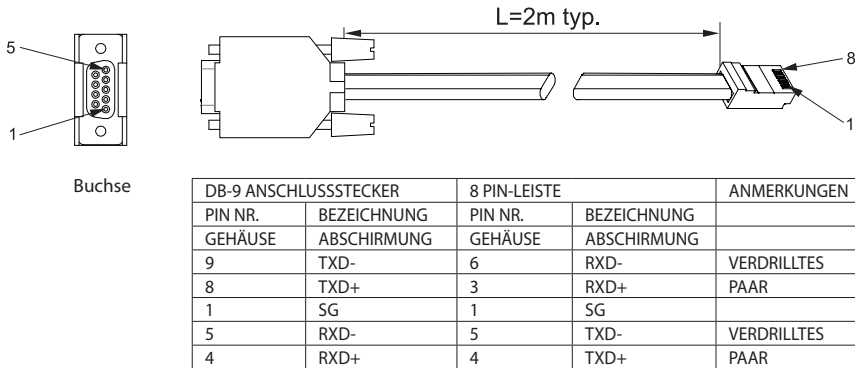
RS485- Kabel mit DB9- Anschlussstecker (P/N: Z/485-9)
